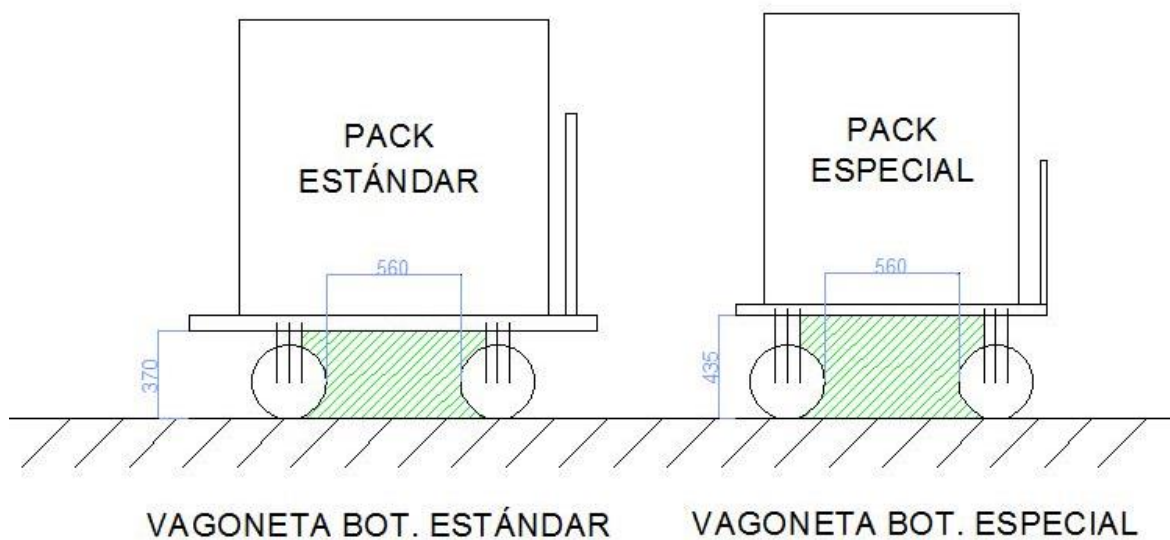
Vista en alzado de las mesas de carga de la instalación
